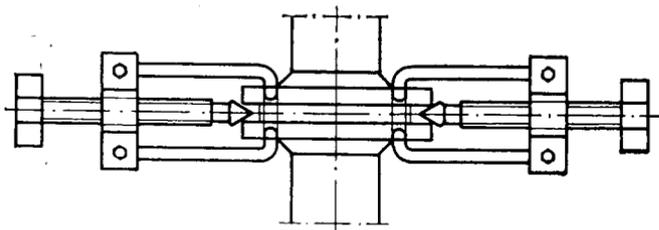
Винтовое приспособление для раздвижки фланцев.
